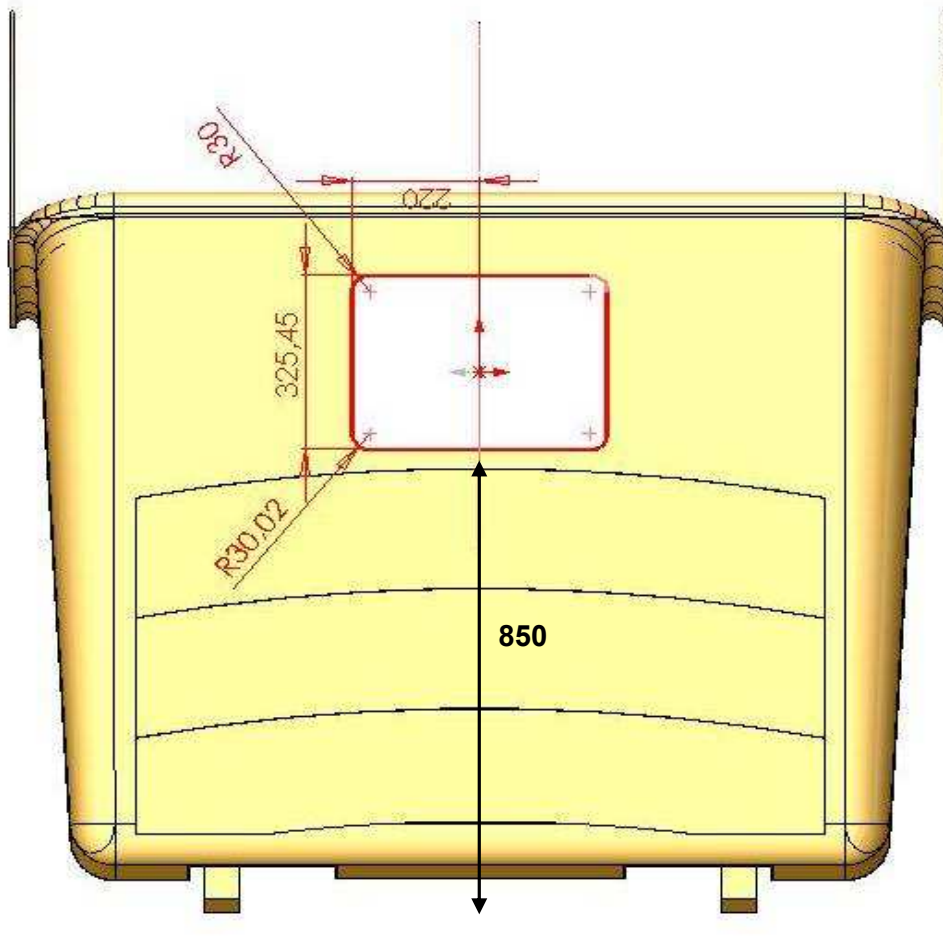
Dimensions del forat practicat en el frontal del contenidor.
